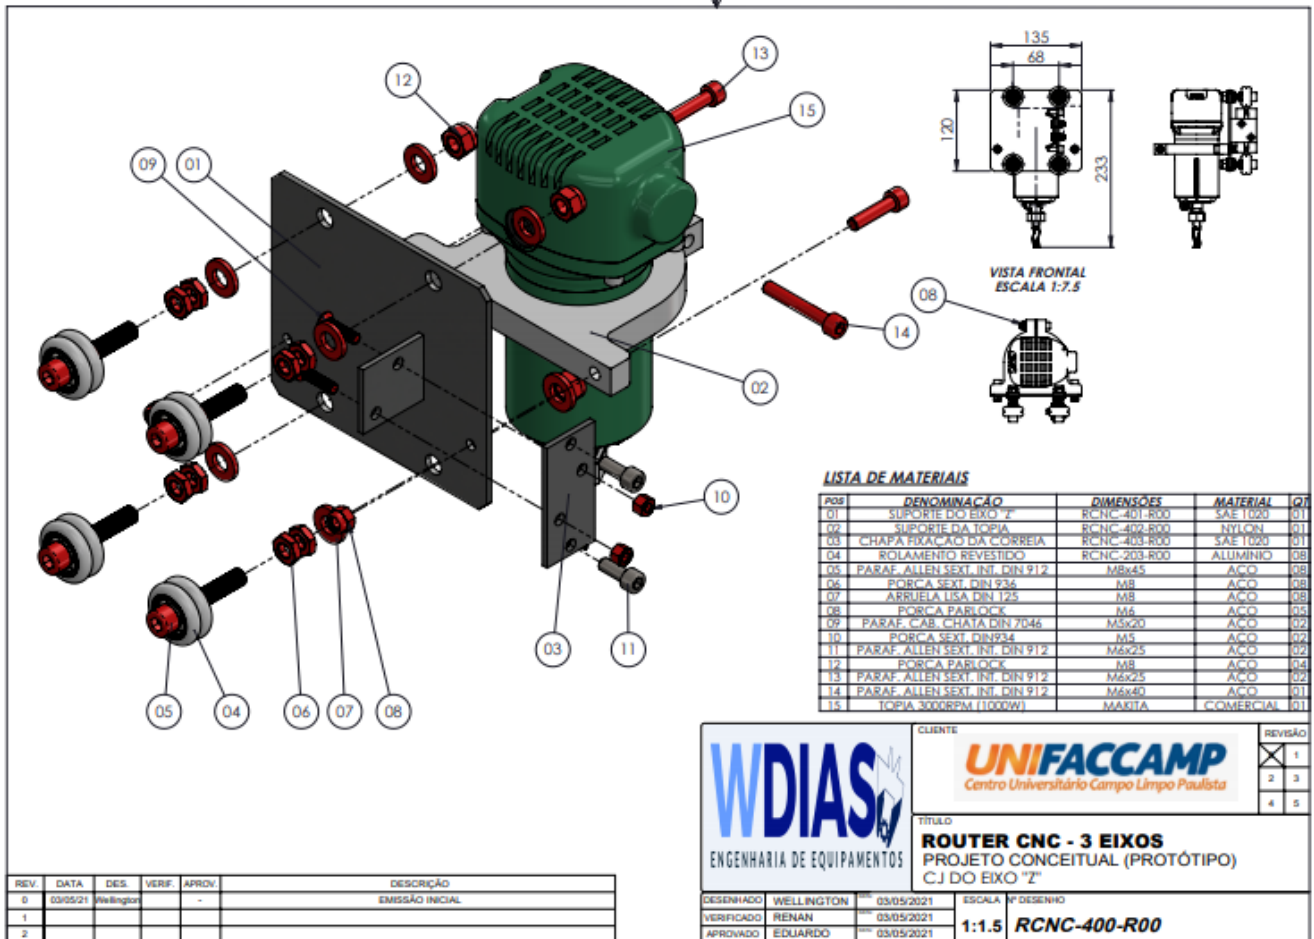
Desenho 2D da montagem do eixo "Z" – com descrição de componentes e materiais.
